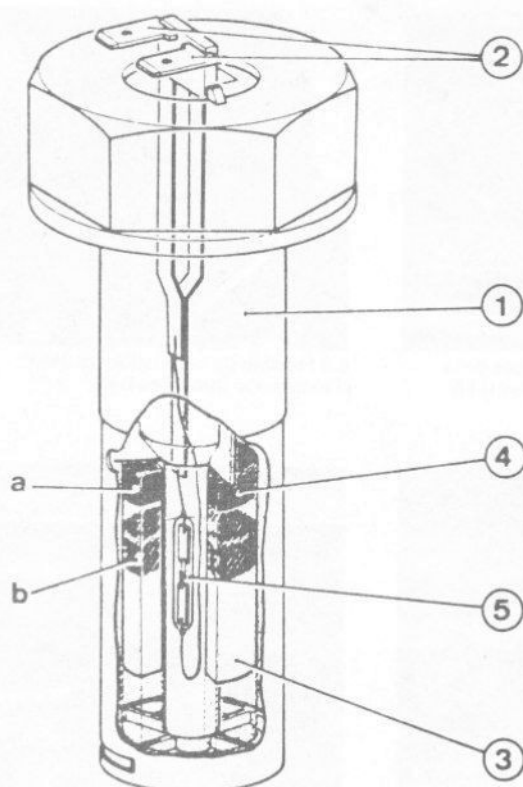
Coupe du contacteur de niveau d'eau (Sec 8)
